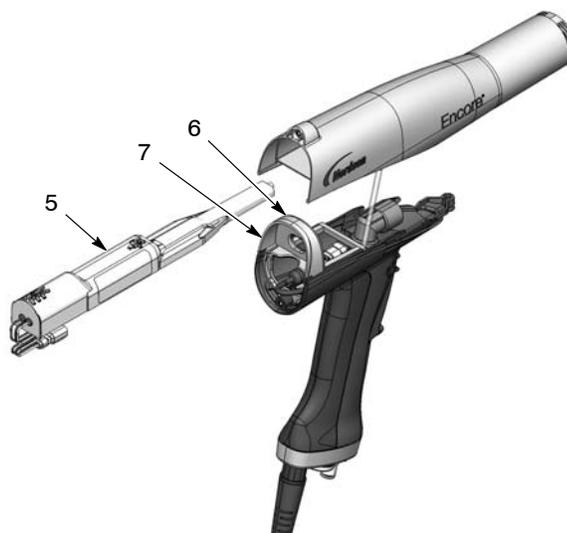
Извлечение блока питания из корпуса распылителя
